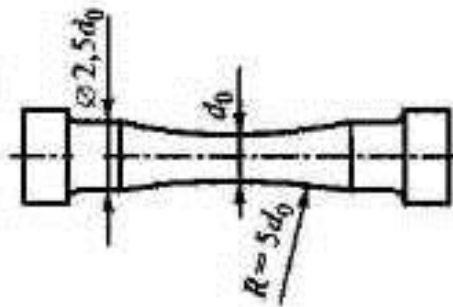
Образец из хрупкого материала для испытаний на растяжение
